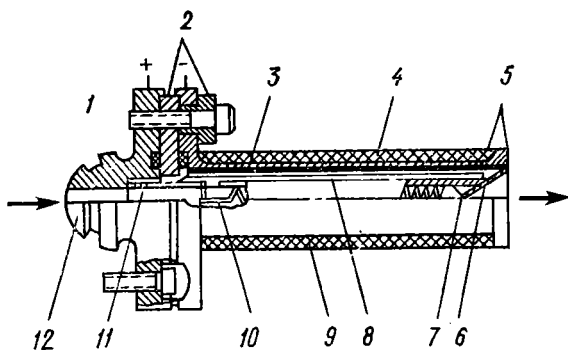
Электронагревный двигатель со спиральным нагревателем: 1 — уплотнения; 2 — изоляторы; 3 — вакуум; 4 — внешний корпус; 5 — сварка электронным лучом; 6 — рениевое сопло; 7 — керамическая проставка; 8 — рениевая трубка; 9 — изоляция; 10 — рениевая спираль нагревателя; 11 — электрическое соединение и компенсация теплового расширения; 12 — направляющий фланец
